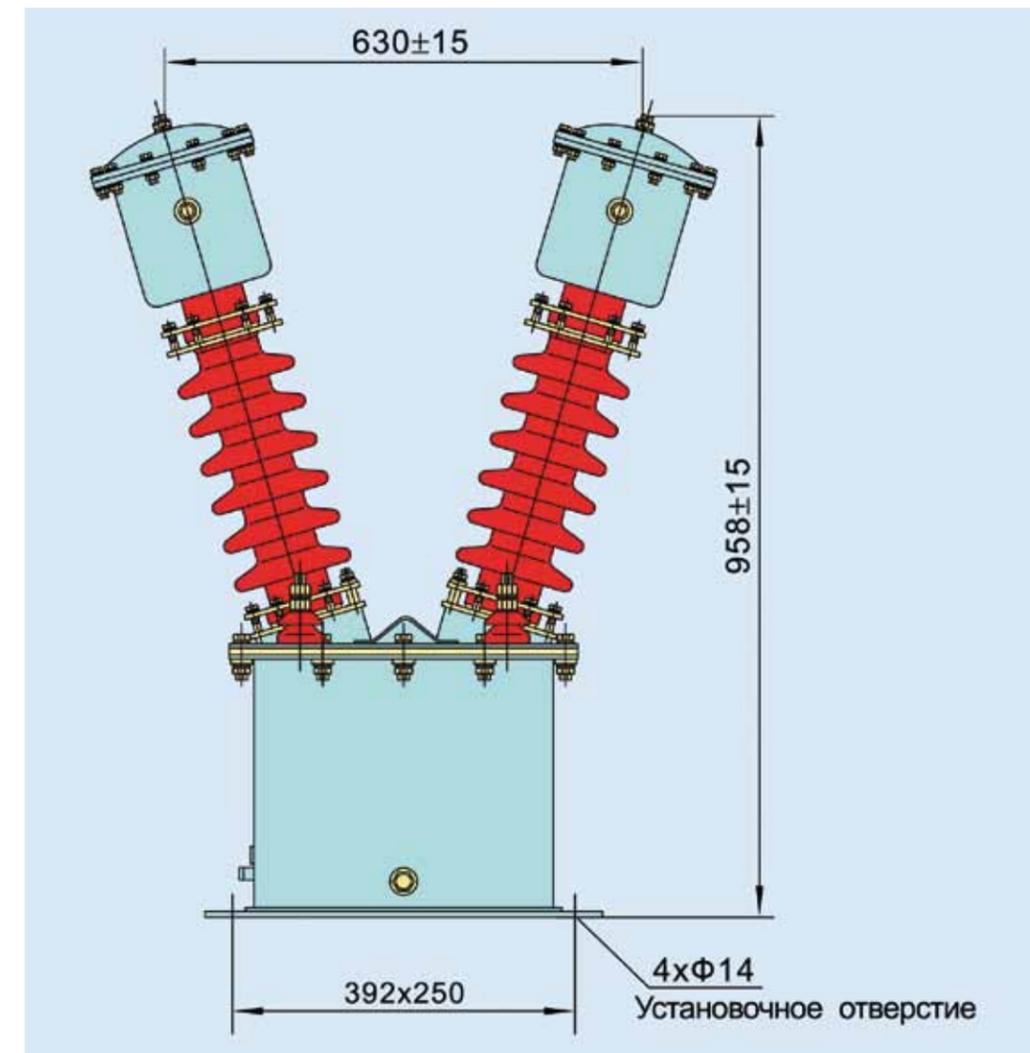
Внешний вид и размеры трансформатора напряжения JDN2-35W2
